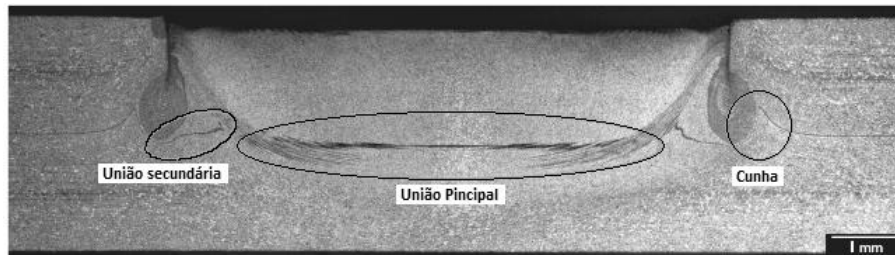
Macrografia de liga AA6181-t4 soldada por FSpW indicando três padrões geométricos frequentes: União Principal, união secundária e Cunha.
